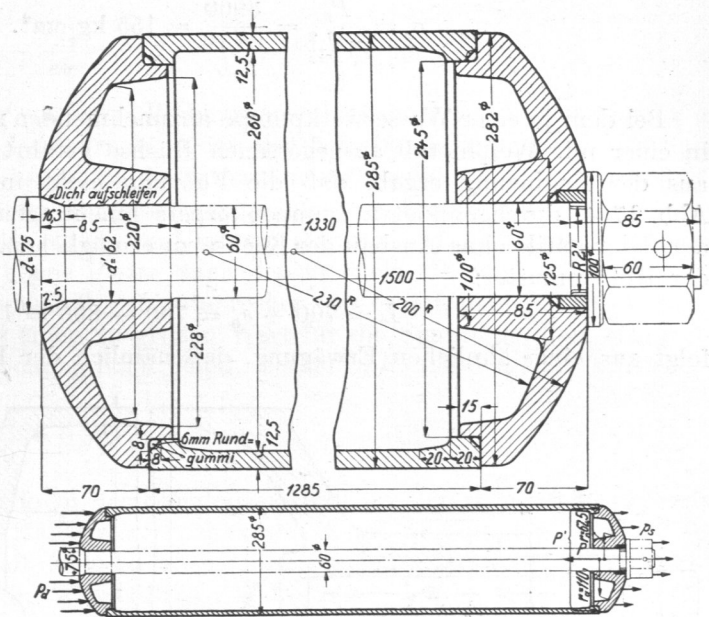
Pumpenkolben zur Wasserwerkmaschine Tafel I.
